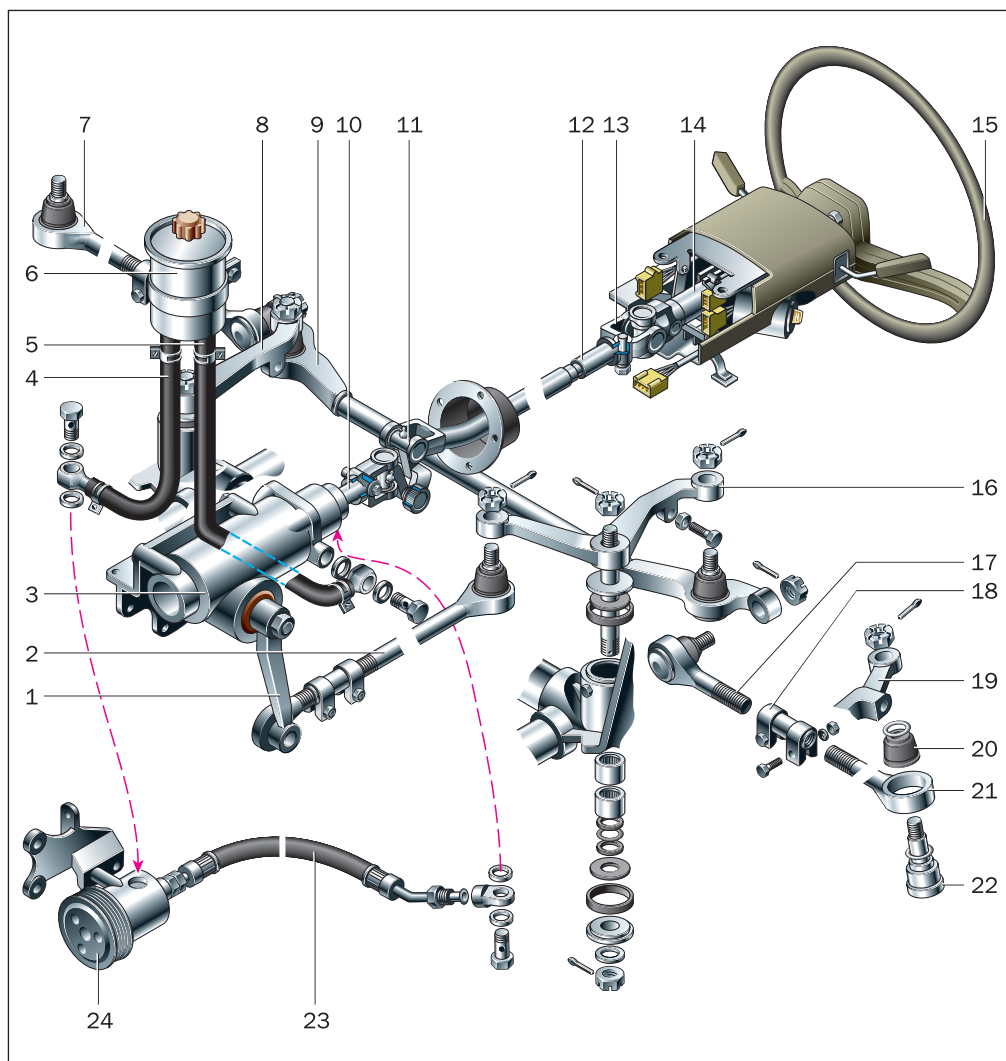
Рулевое управление с гидроусилителем: 1 — рулевая сошка; 2 — продольная рулевая тяга; 3 — рулевой механизм; 4 — всасывающий шланг; 5 — сливной шланг; 6 — бак; 7 — правая боковая рулевая тяга; 8 — правый маятниковый рычаг; 9 — поперечная рулевая тяга; 10 — входной вал рулевого механизма; 11 — нижний карданный шарнир; 12 — карданный вал; 13 — верхний карданный шарнир; 14 — вал рулевой колонки; 15 — рулевое колесо; 16 — левый маятниковый рычаг; 17, 21 — наконечники левой боковой тяги; 18 — хомут регулировочной трубки; 19 — левый рычаг рулевой трапеции; 20 — чехол шарнира; 22 — шарнир; 23 — нагнетательный шланг; 24 — насос гидроусилителя
